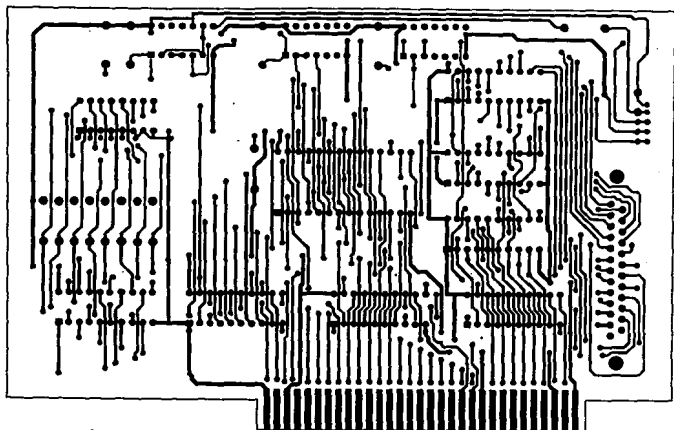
Circuito impreso de la tarjeta simulador de ROM lado de soldadura
